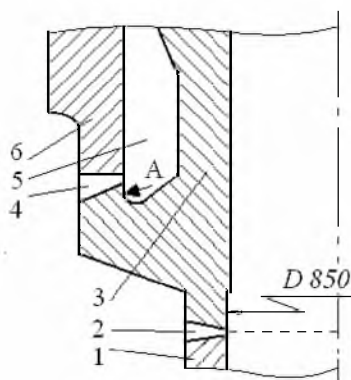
Фрагмент узла приварки: 1 – часть ГЦТ; 2, 4 – сварные швы; 3 – коллектор; 5 – карман; 6 – патрубок ПГ; А – место иницирования разрушения.
